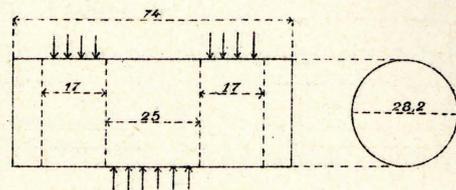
Provetta cilindrica, tipo B. — Scala di 1/2.
